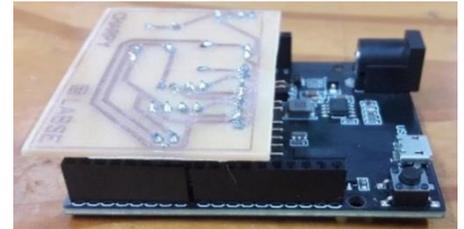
Circuito PCB de la placa acondicionadora de señal.
